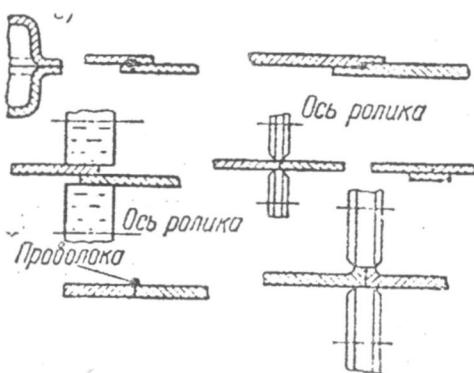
Типы изделий, получаемых шовной сваркой
